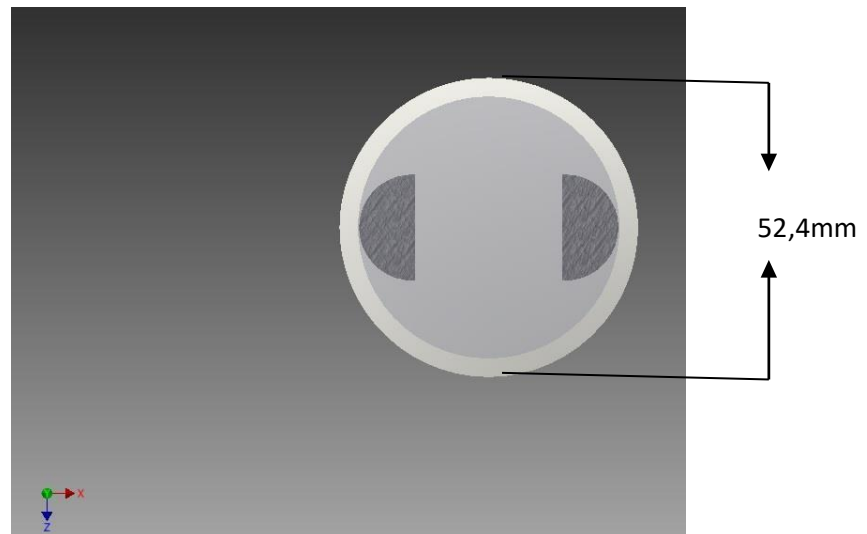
Silinder dan piston 50 mm tampak depan
